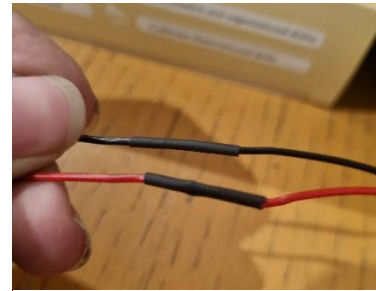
Fotografía de cables con tubo retráctil aislante antes de aplicar calor
